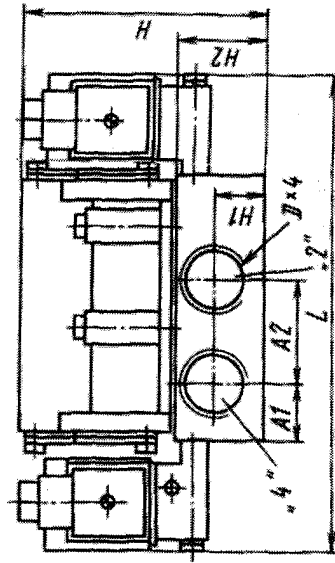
Габаритные и присоединительные размеры пневмораспределителей резьбового исполнения B64-13A-03, M4-14A-03, B64-15A-03
